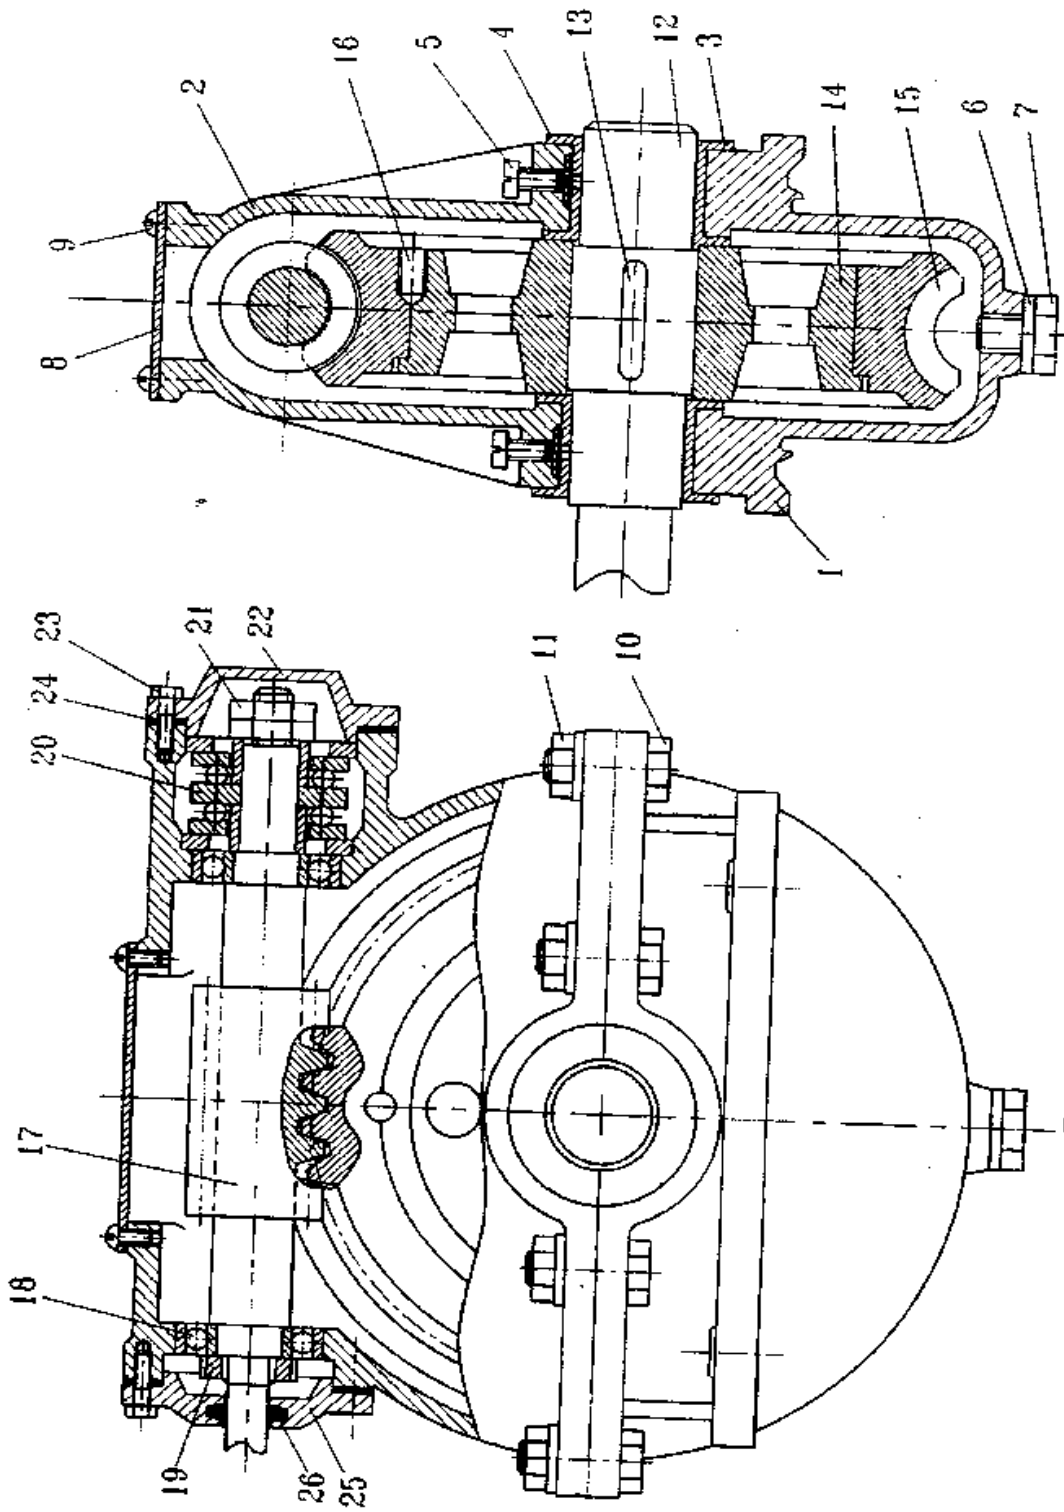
Складальне креслення черв'ячного редуктора [27]
